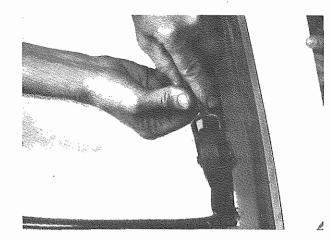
Spianare it sigillante con la rotella Flattening the sealing using the proper roller
